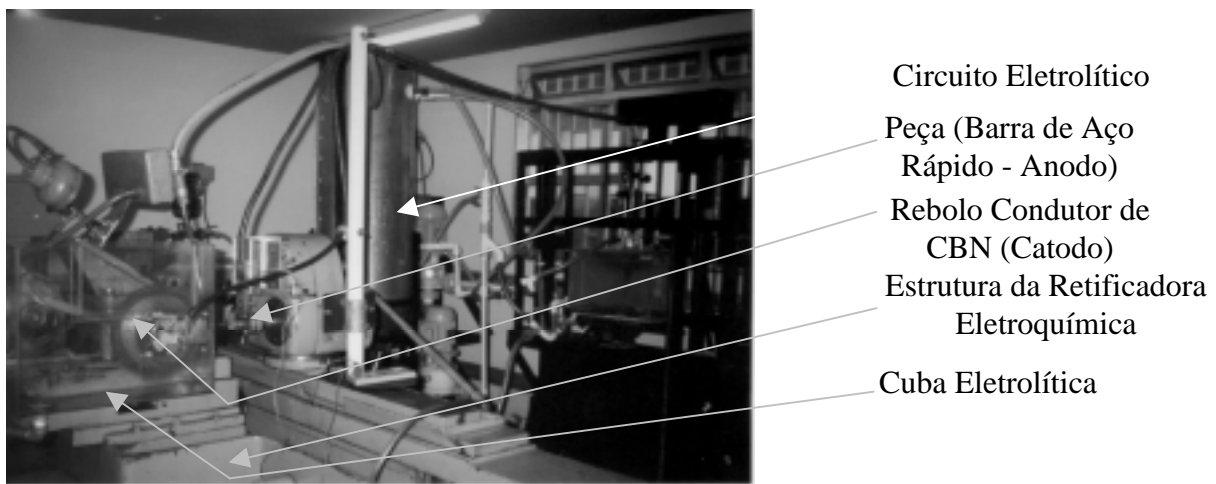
Vista principal e final da retificadora eletroquímica desenvolvida a partir de uma retificadora cilíndrica universal.
